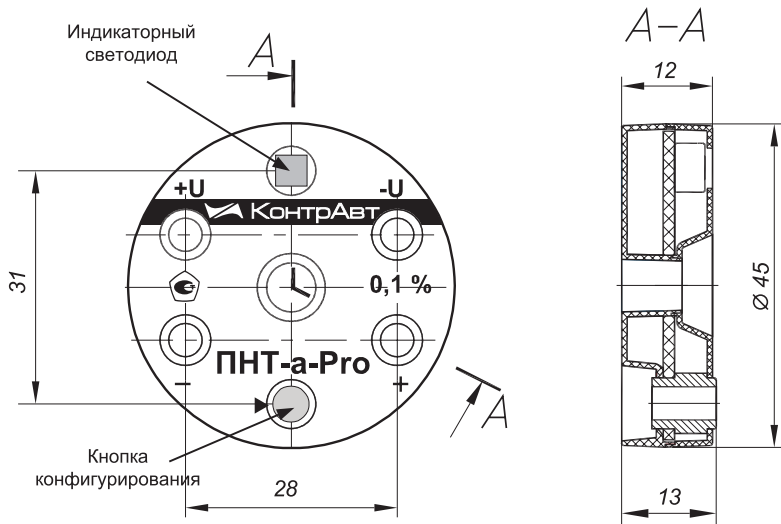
Внешний вид и габаритные размеры преобразователя
